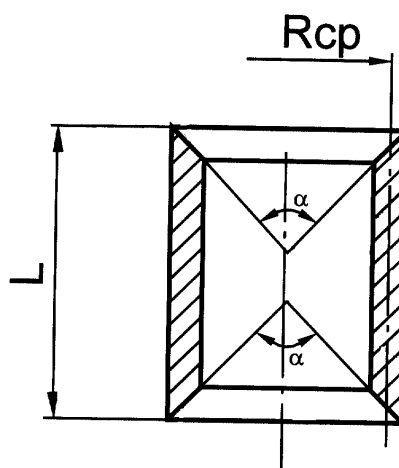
Эскиз заготовки:  $R_{cp}$  – средний диаметр заготовки,  $L$  – длина заготовки
